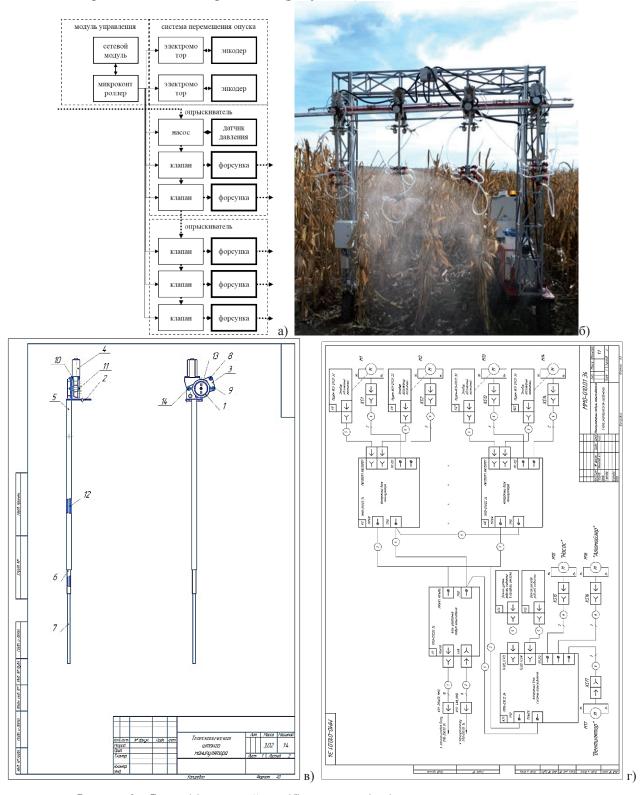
Схема (а), внешний вид (б) и чертежи (в, г) манипулятора опрыскивателя
